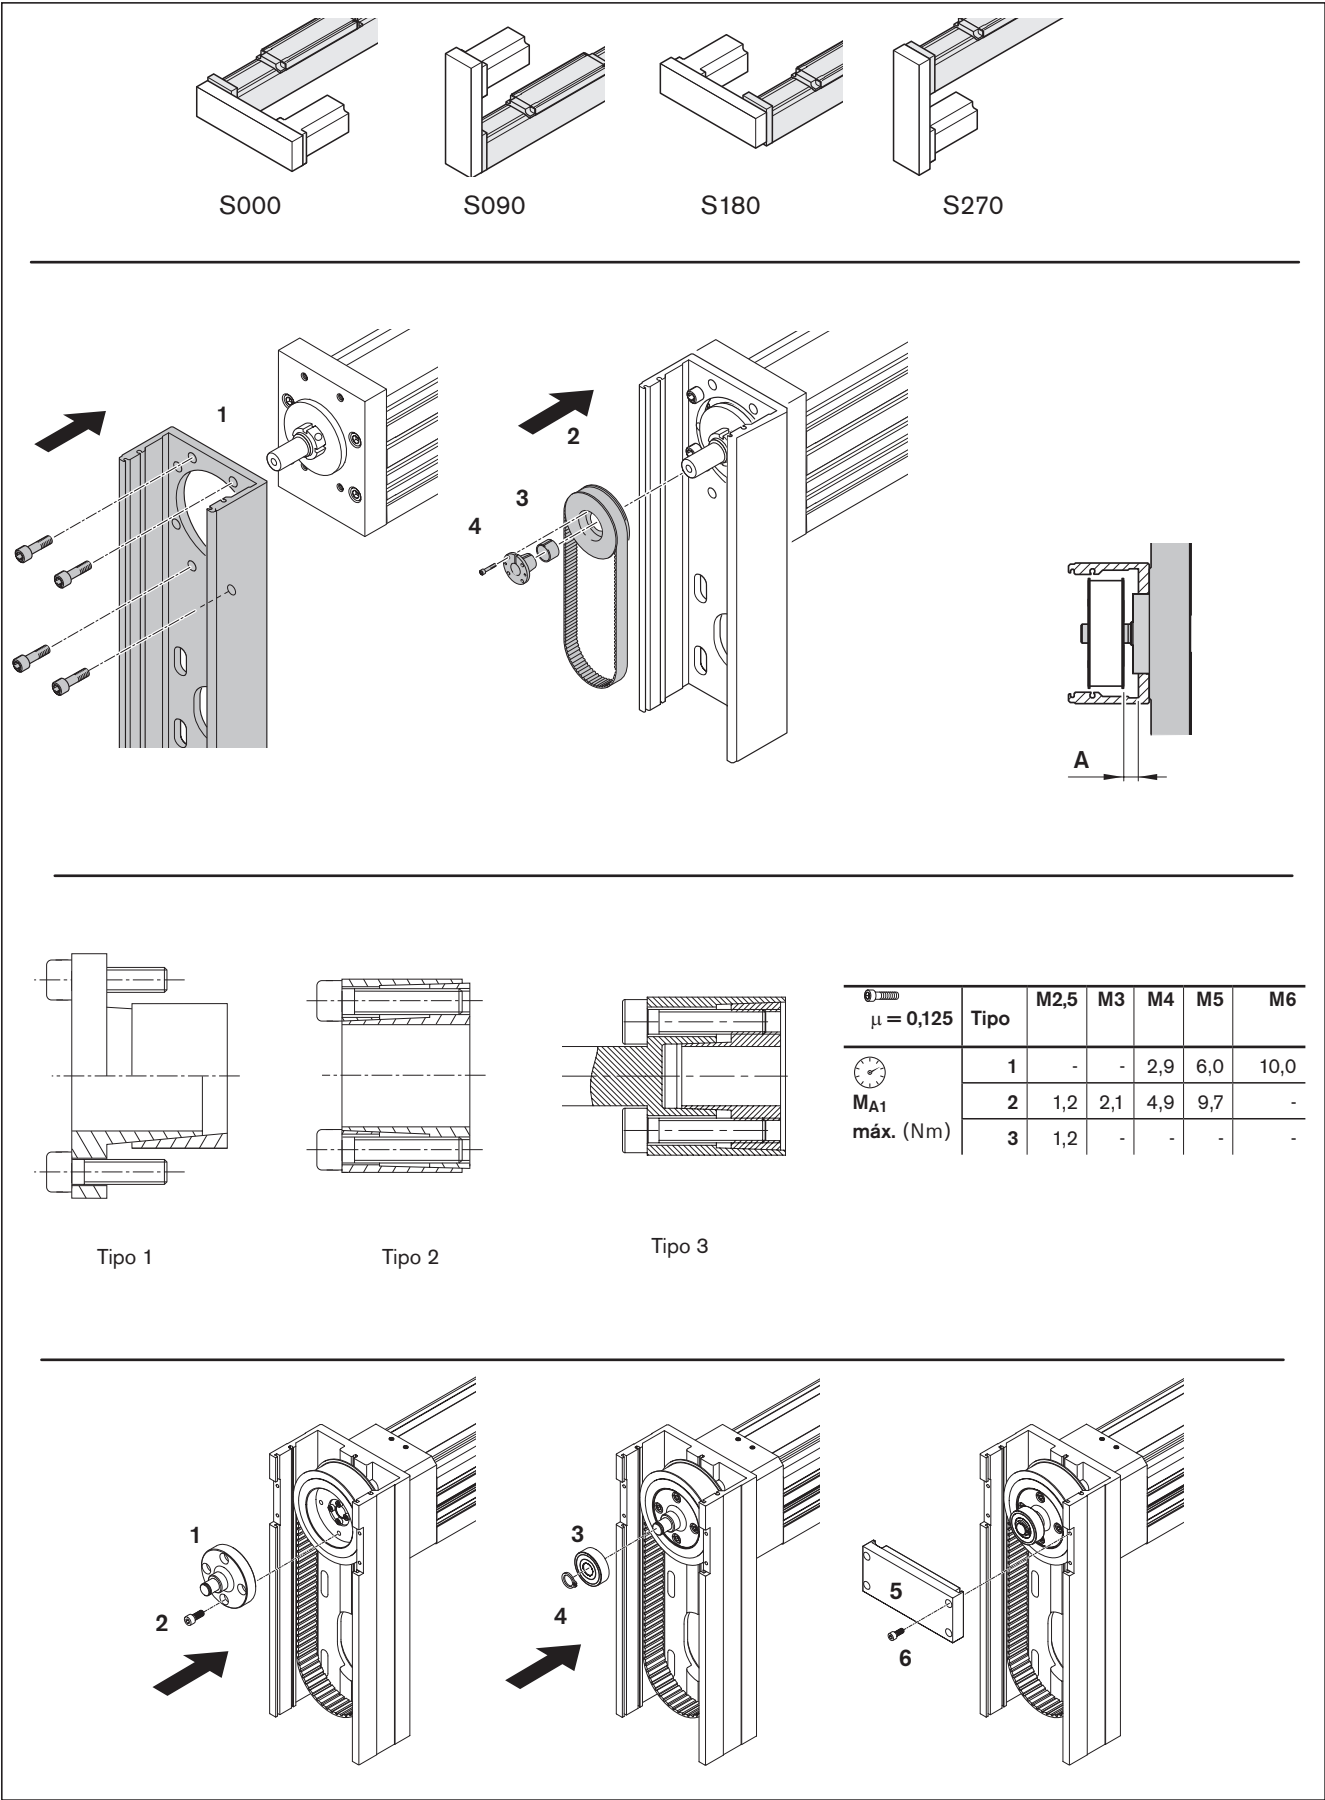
Montaje de la transmisión por correa/montaje de la primera polea de la correa/montaje del rodamiento opuesto
